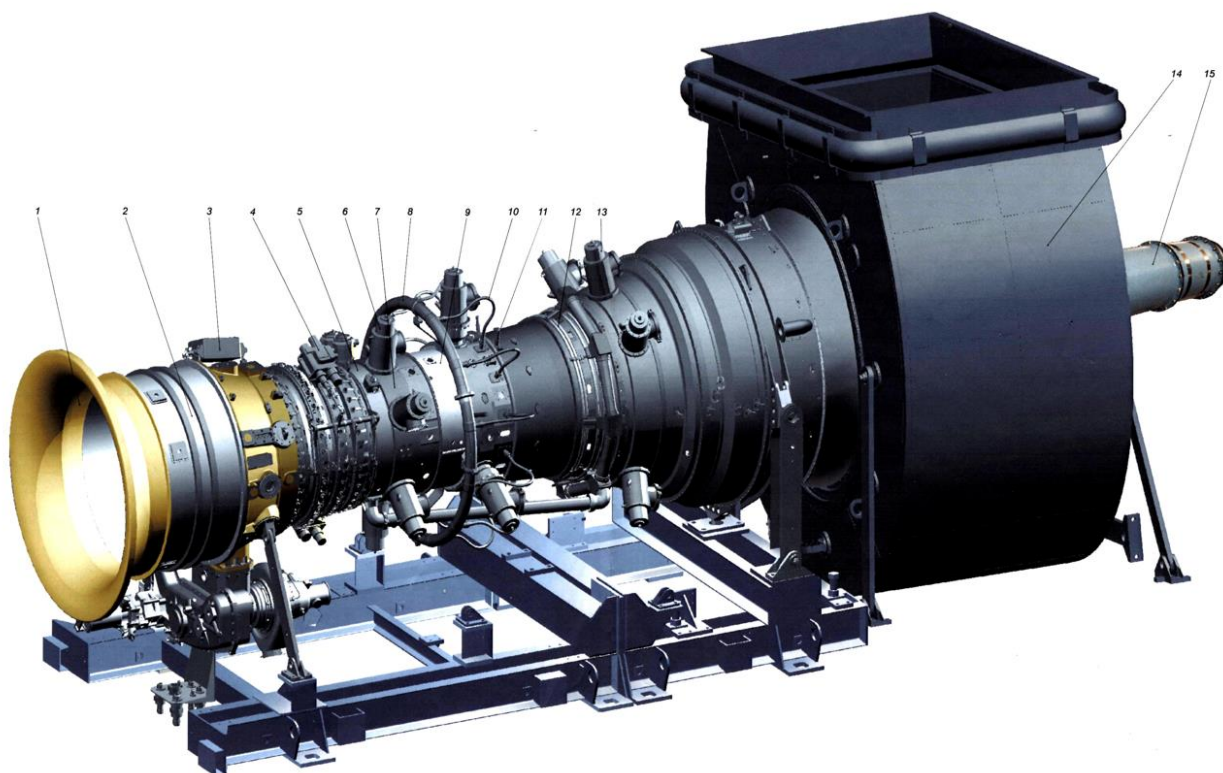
ГТУ. 1- Входное устройство. 2 – Корпус промывки. 3 – Агрегат зажигания. 4 – Электропривод лопаток входного направляющего аппарата. 5 – Корпус компрессора передний. 6 – клапаны перепуска воздуха. 7 – корпус перепуска и отборов. 8- коллектор газовый. 9 – корпус обдува. 10- трубопровод подвода газа к форсункам. 11 – свеча зажигания с кожухом. 12 – трубы подвода охлаждающего воздуха. 13 – клапаны перепуска газа. 14 – выхлопное устройство. 15 – Трансмиссия
